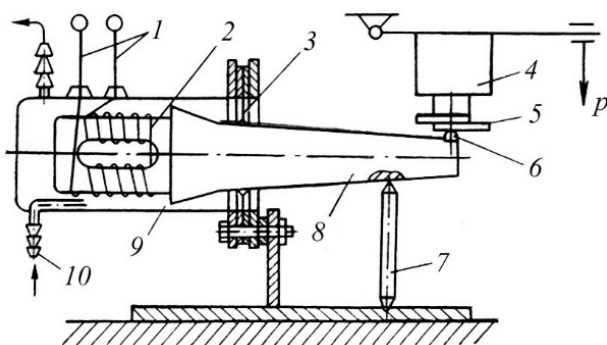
Схема установки для точкового зварювання ультразвуком:
